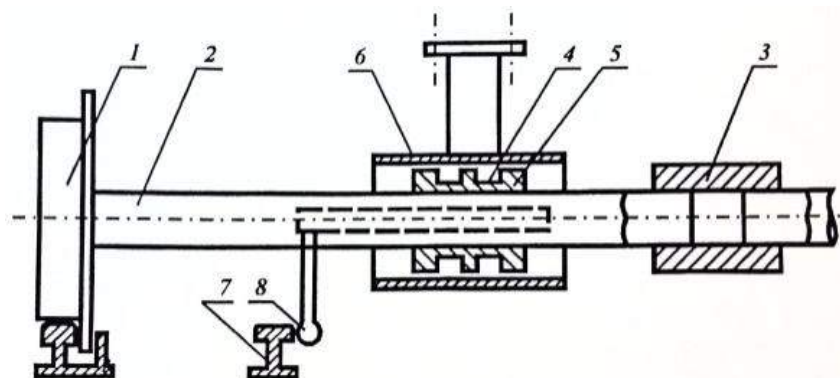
Схема колесной пары: 1 – колесо; 2 – полуоси; 3 – муфта; 4 – кольцевые канавки; 5 – втулка; 6 – корпус узла фиксации; 7 – направляющие для приводной головки; 8 – приводная головка
